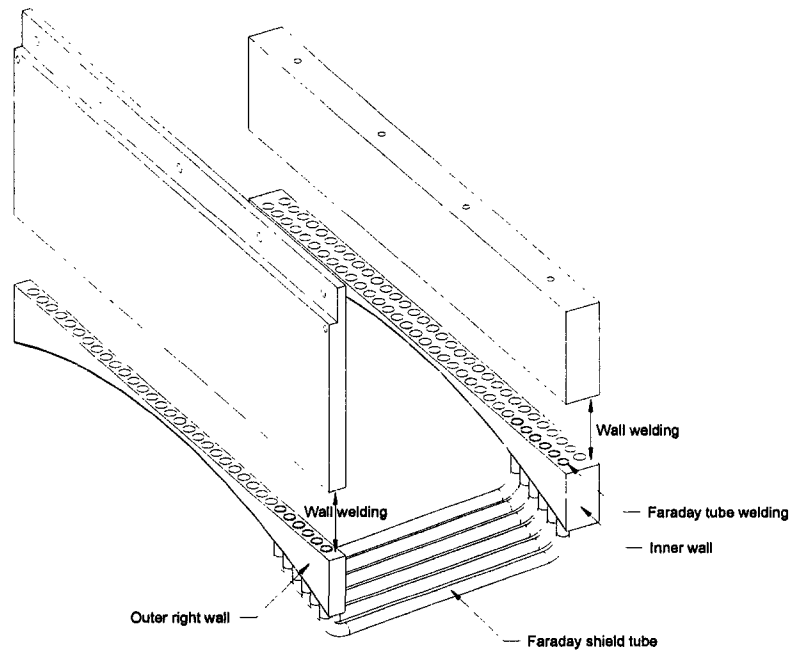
Mounting of Faraday shield tubes on the cavity box.
